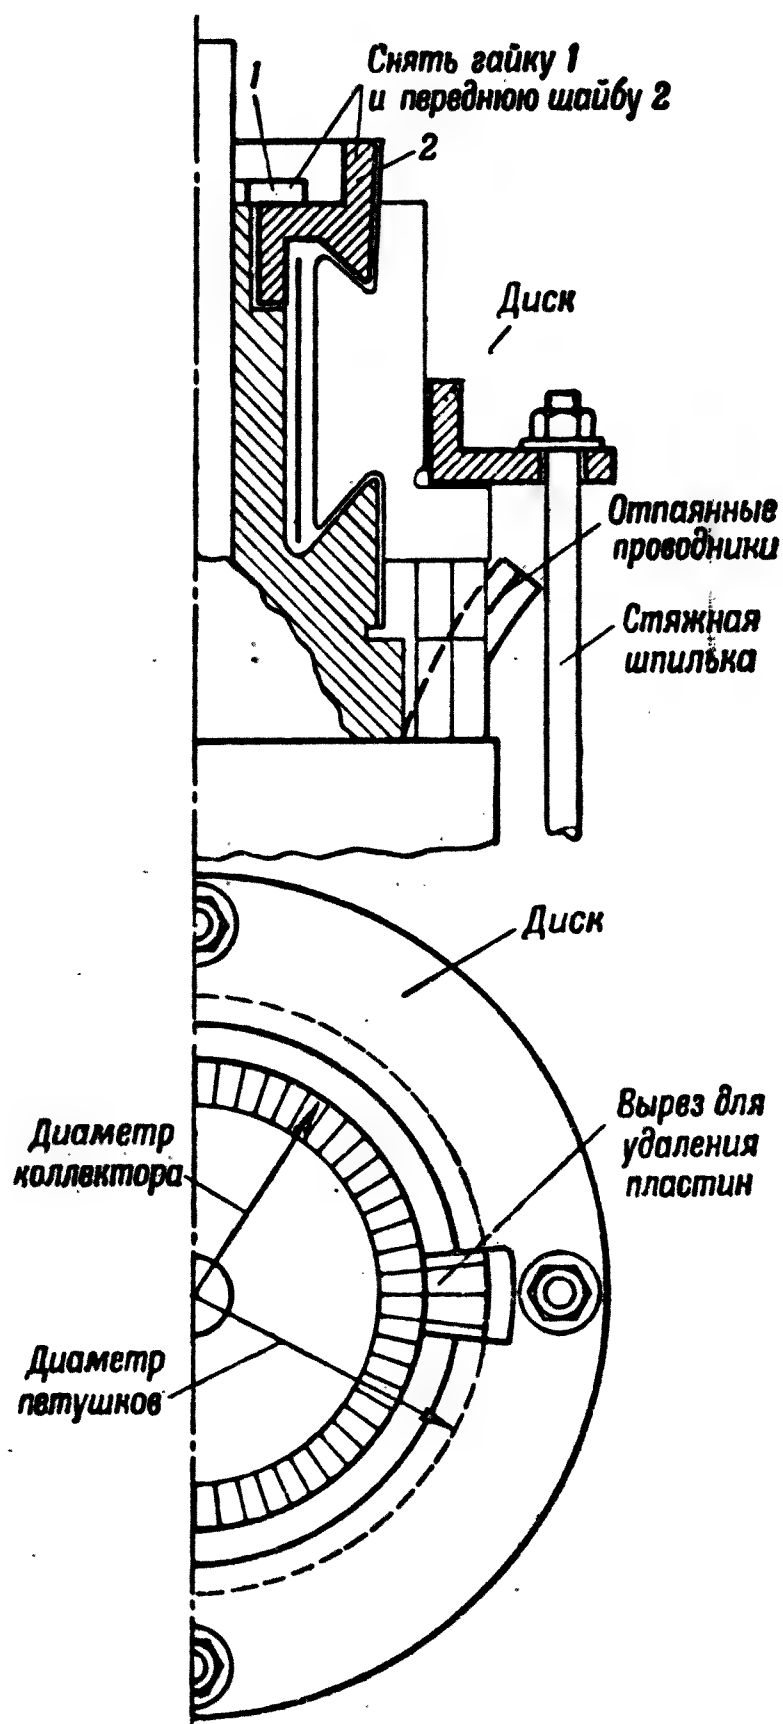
Приспособление для замены неисправных пластин коллектора.
